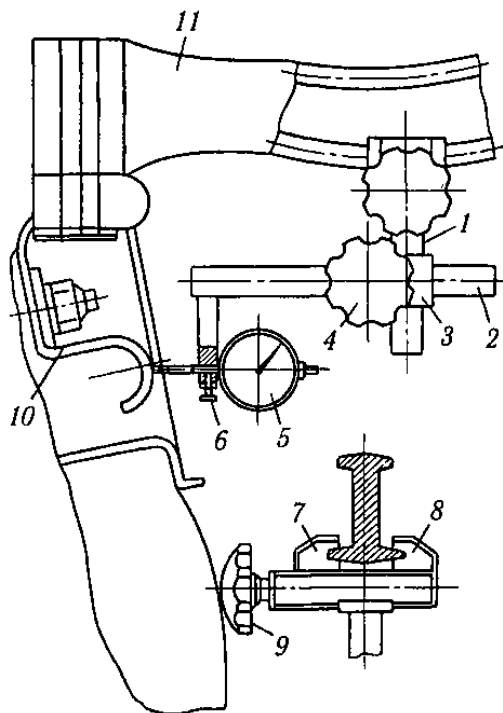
Пристрій для перевірки зазорів у шворневих з'єднаннях:
